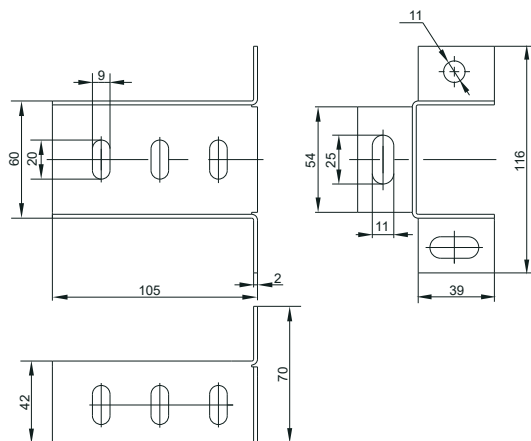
Кронштейн потолочный для П-профиля SSU / Figure C.2 – SSU ceiling bracket for U-shaped profile
